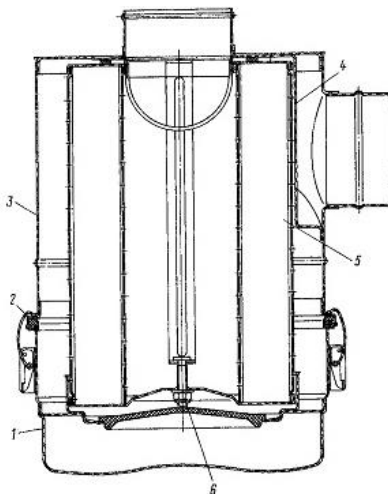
Воздухоочиститель: 1 – крышка; 2 – прокладка крышки; 3 – корпус; 4 – пылеотбойник; 5 – элемент фильтрующий; 6 – гайка фильтрующего элемента
